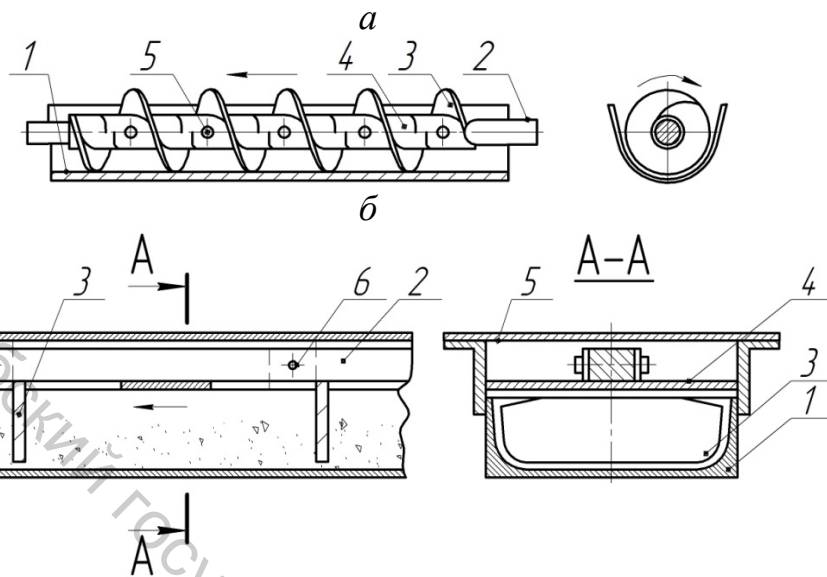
Шнековый (а) и скребковый (б) конвейеры для удаления стружки
